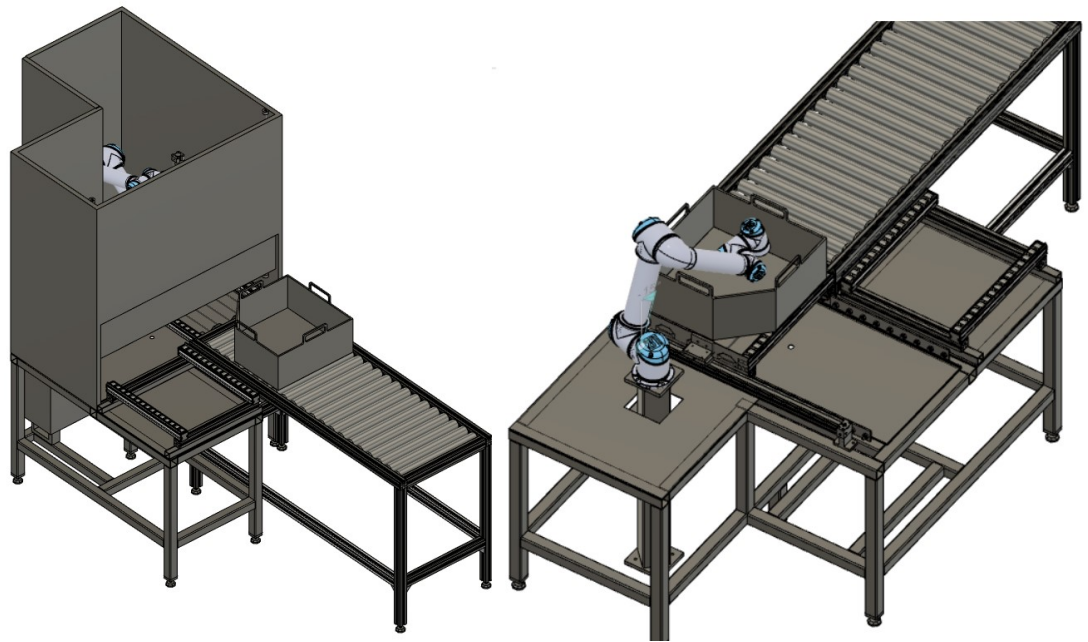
Johdehissillinen automaattioratkaisun layout.
